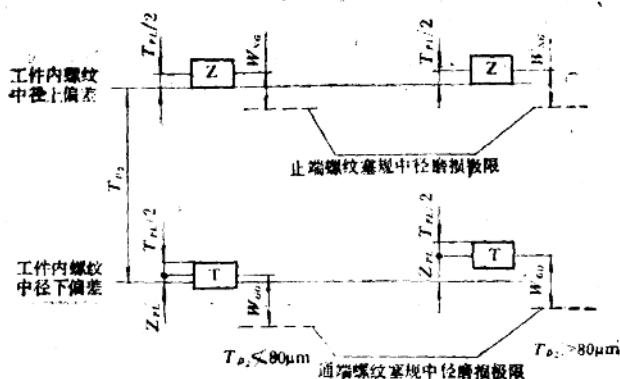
检验工件内螺纹用的螺纹塞规中径公差带图
